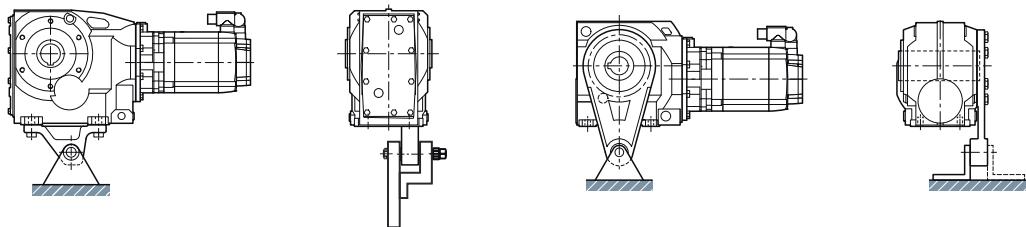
Montagevorschlag für Drehmomentstütze an Fuß und Flansch
